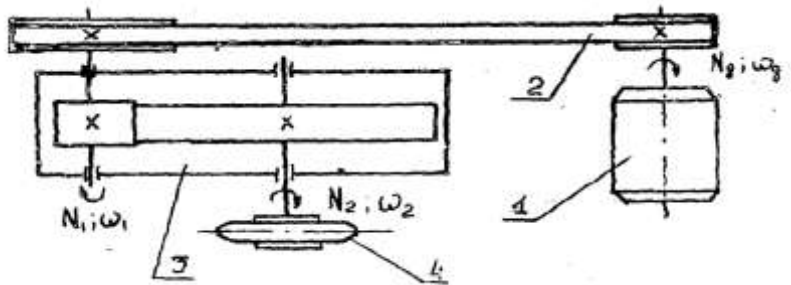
Схема привода. 1 - электродвигатель, 2-ременная передача, 3-зубчатый редуктор,4- звездочка конвейера.
